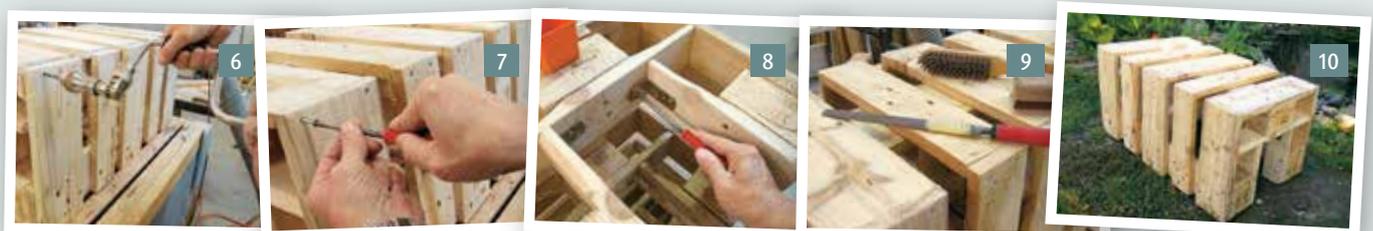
Seitenteile mit dem Mittelteil verschrauben.
